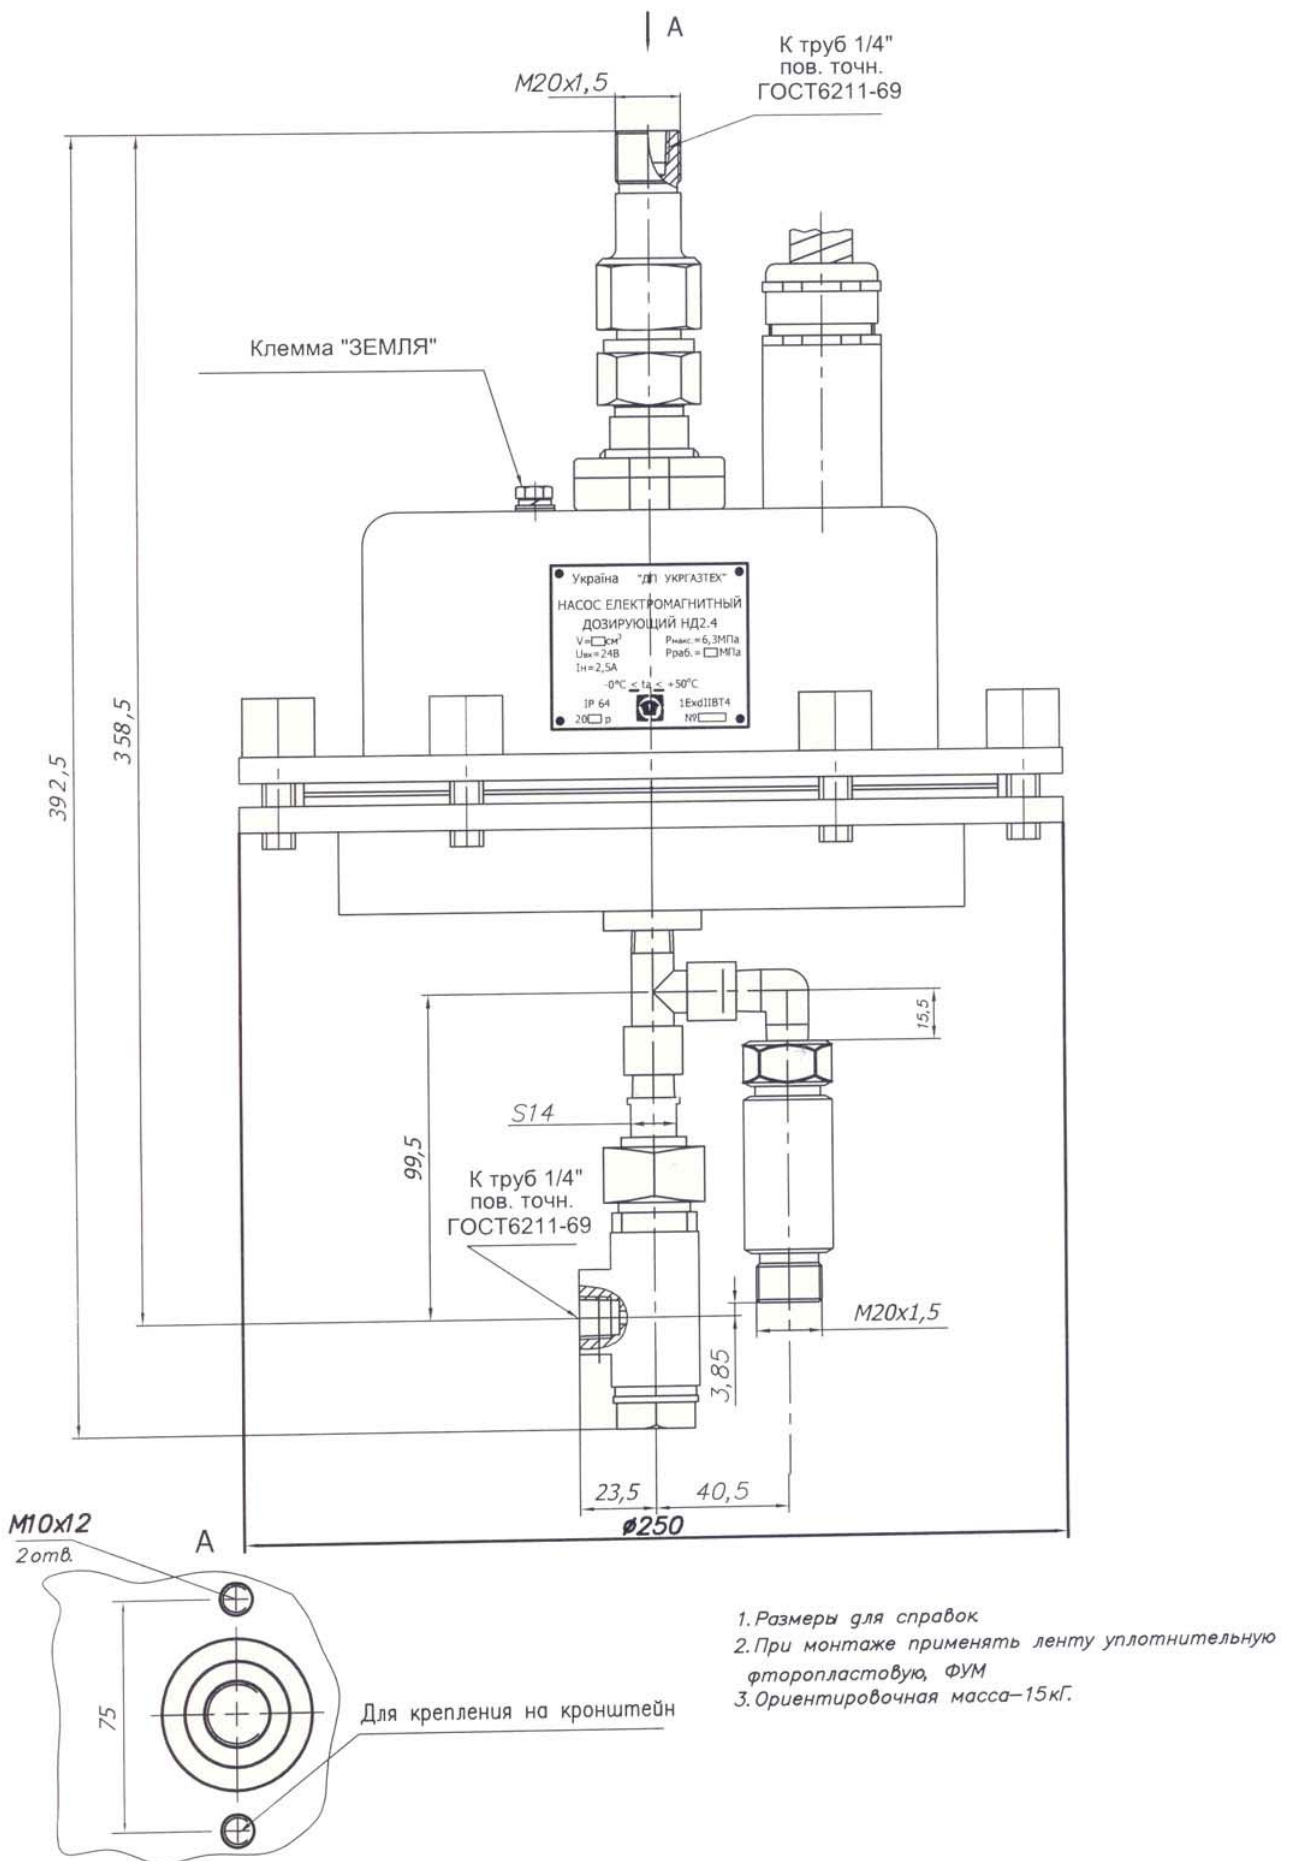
Общий вид (в рабочем положении) и габаритные и присоединительные размеры насоса НЗ
